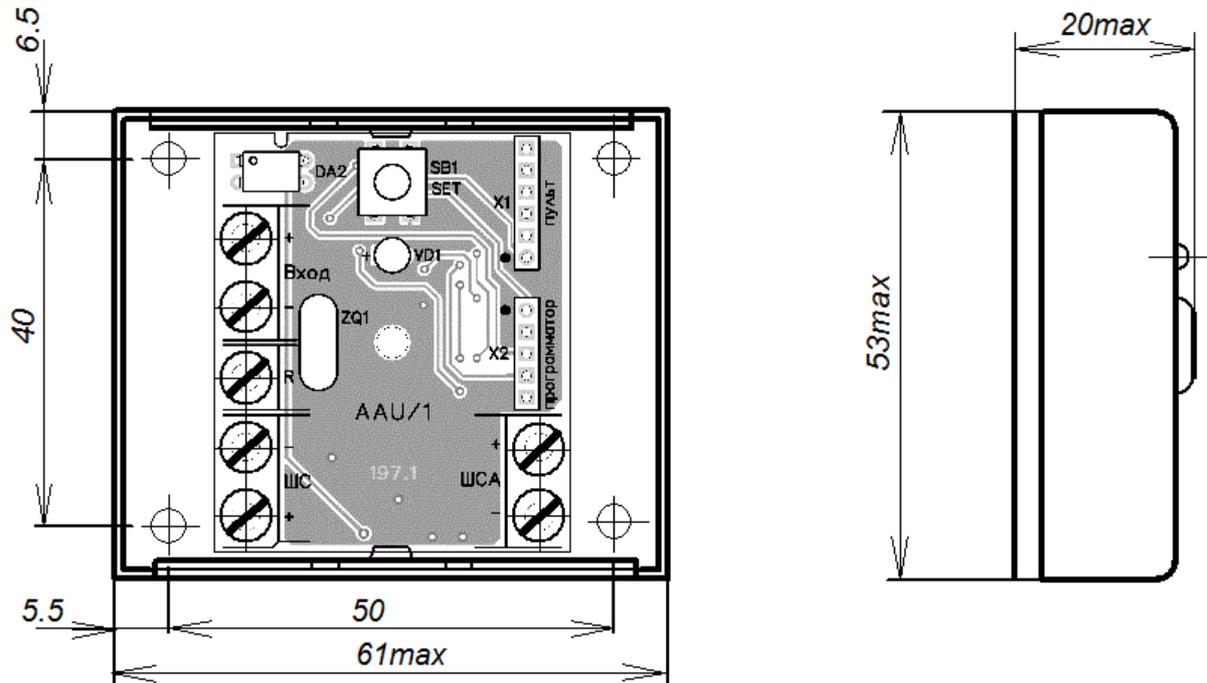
Внешний вид, габаритные и установочные размеры ААУ
